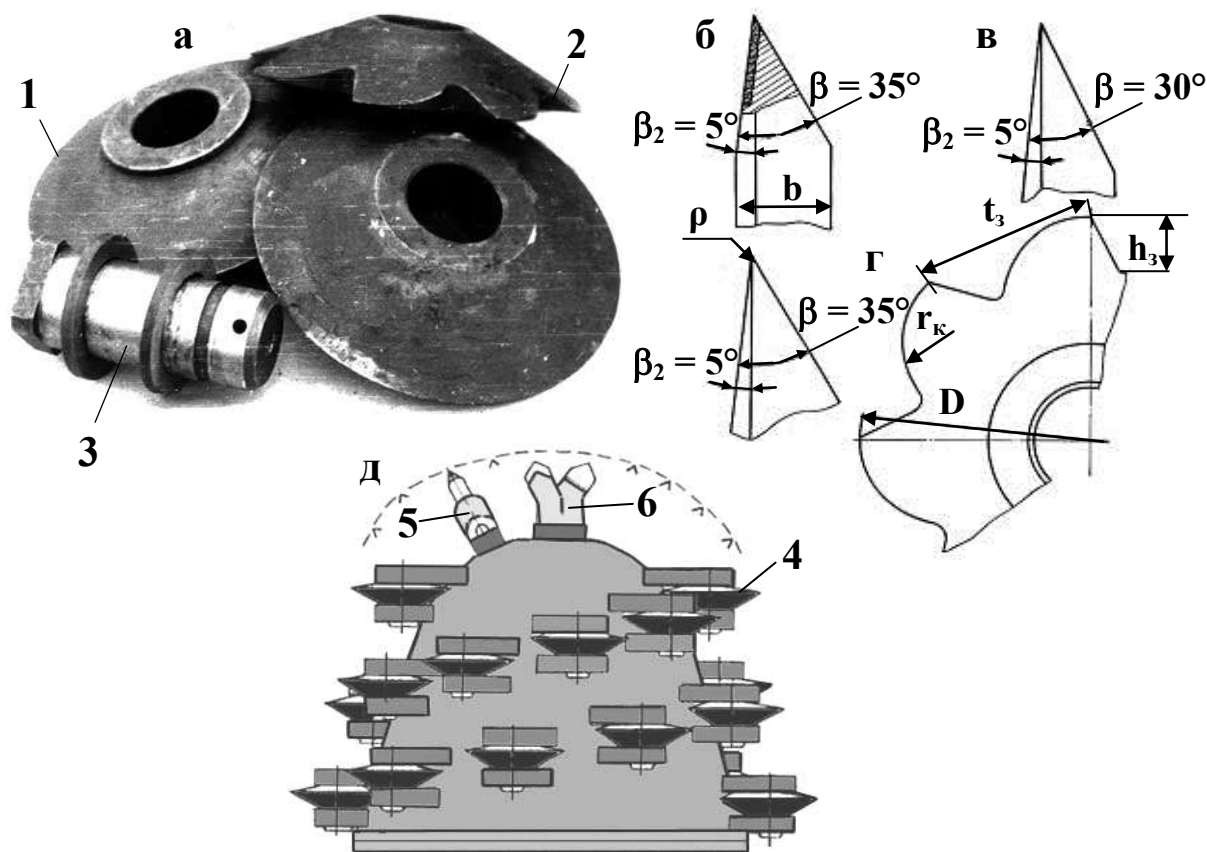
Дисковый шарошки и коронка: а – общий вид дисков (1 – сплошная кромка; 2 – прерывистая кромка переменной кривизны; 3 – ось вращения); б, в, г – режущие кромки дисков; д – коронка, включающая диски 4, резцы 5 и забурник 6
